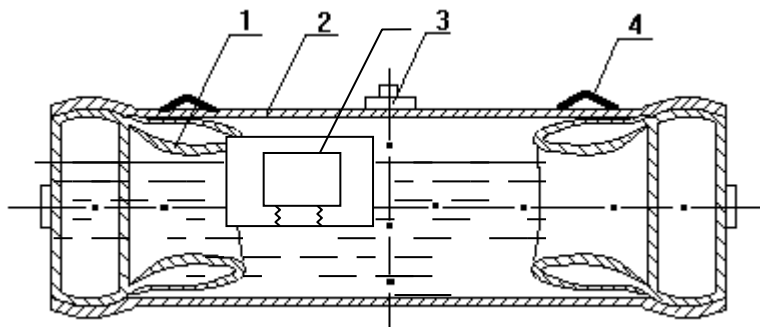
Схема резервуара с плавающим в контейнере образцом стрелкового оружия на упругой основе (1 – вспомогательные рукава, 2 – корпус резервуара, 3 – сливное-заливное приспособление, 4 – крепление для перемещения резервуара, 5 – образец стрелкового оружия).
